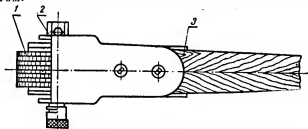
Державка с набором шарошек-звездочек для правки шлифовальных кругов:
